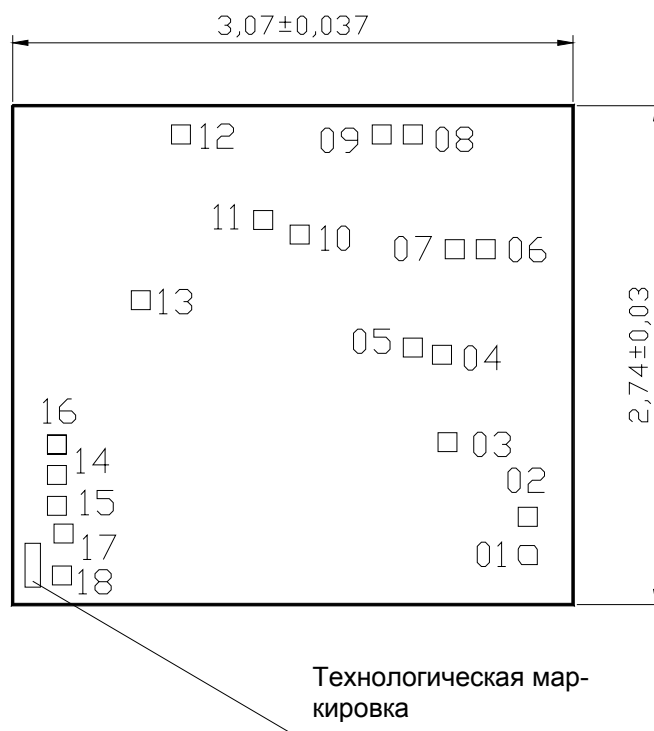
Габаритные размеры корпуса 1509.9-А
